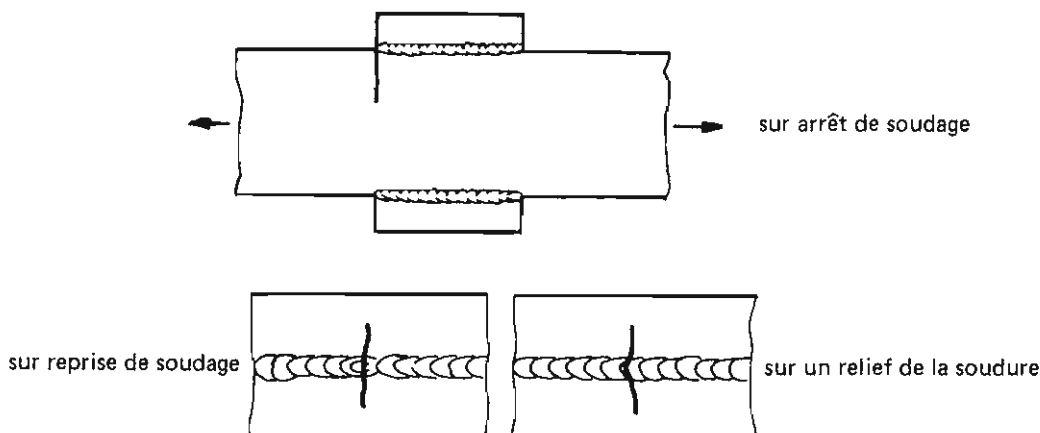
Fissuration par fatigue d'une soudure bout à bout longitudinale.
